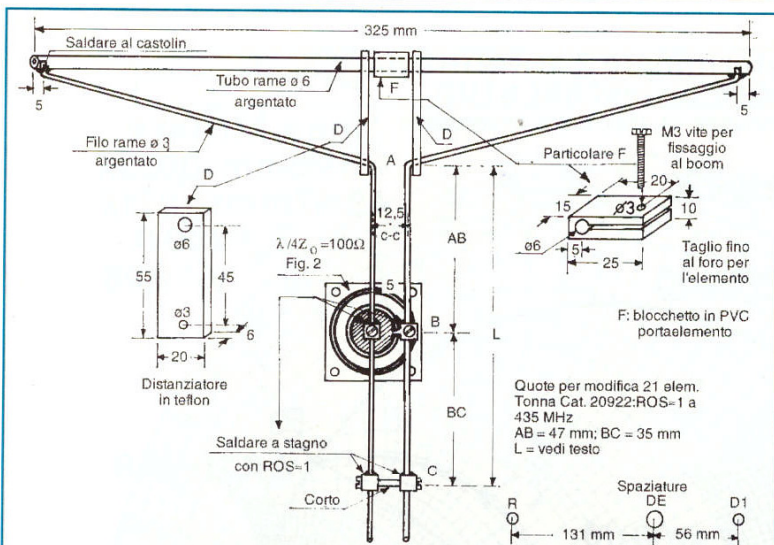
• Disegno meccanico e costruttivo del dipolo per 432 MHz con delta match e universal stub
